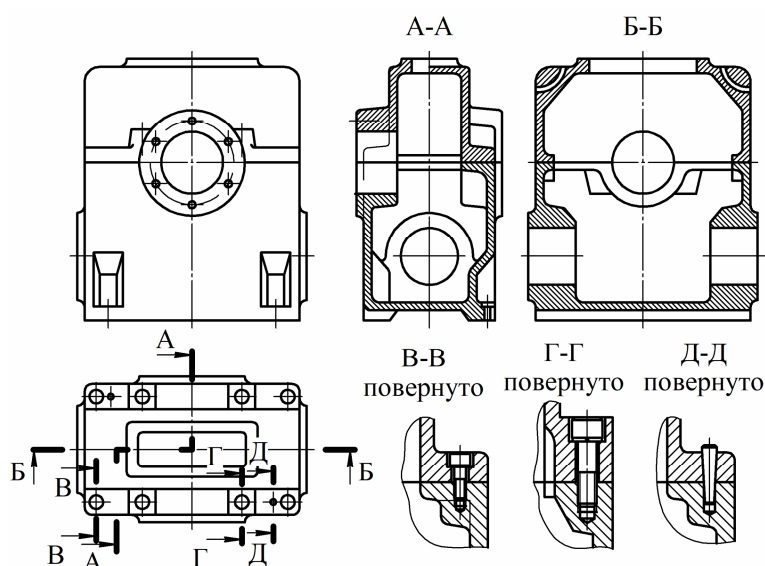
Корпус червячного редуктора с разъемом по оси вала колеса
